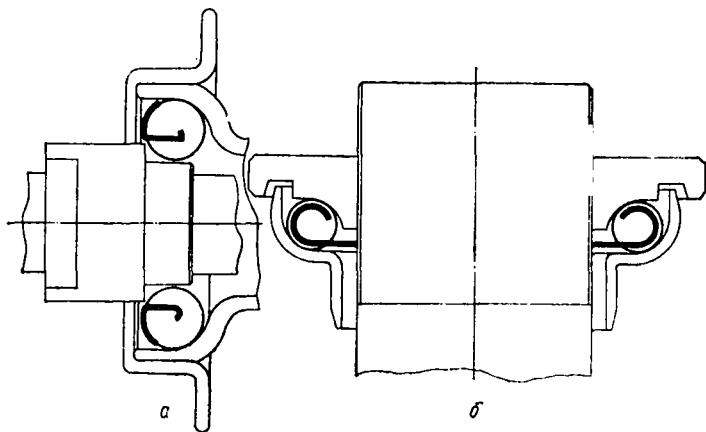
Установка шарикоподшипника (шарики в сепараторе):
